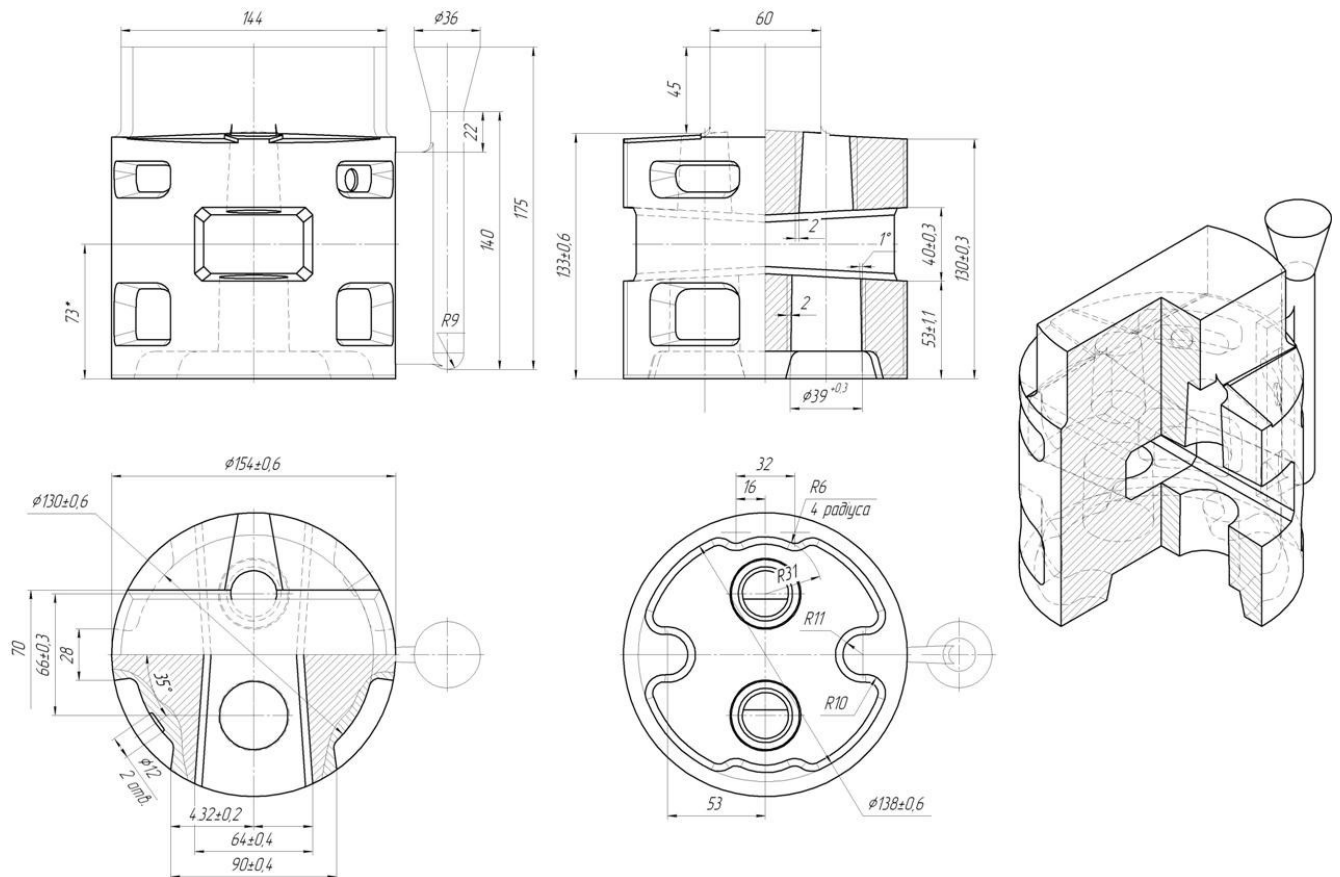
Виливок блоку обойми підшипникової НШ100А-3-05
